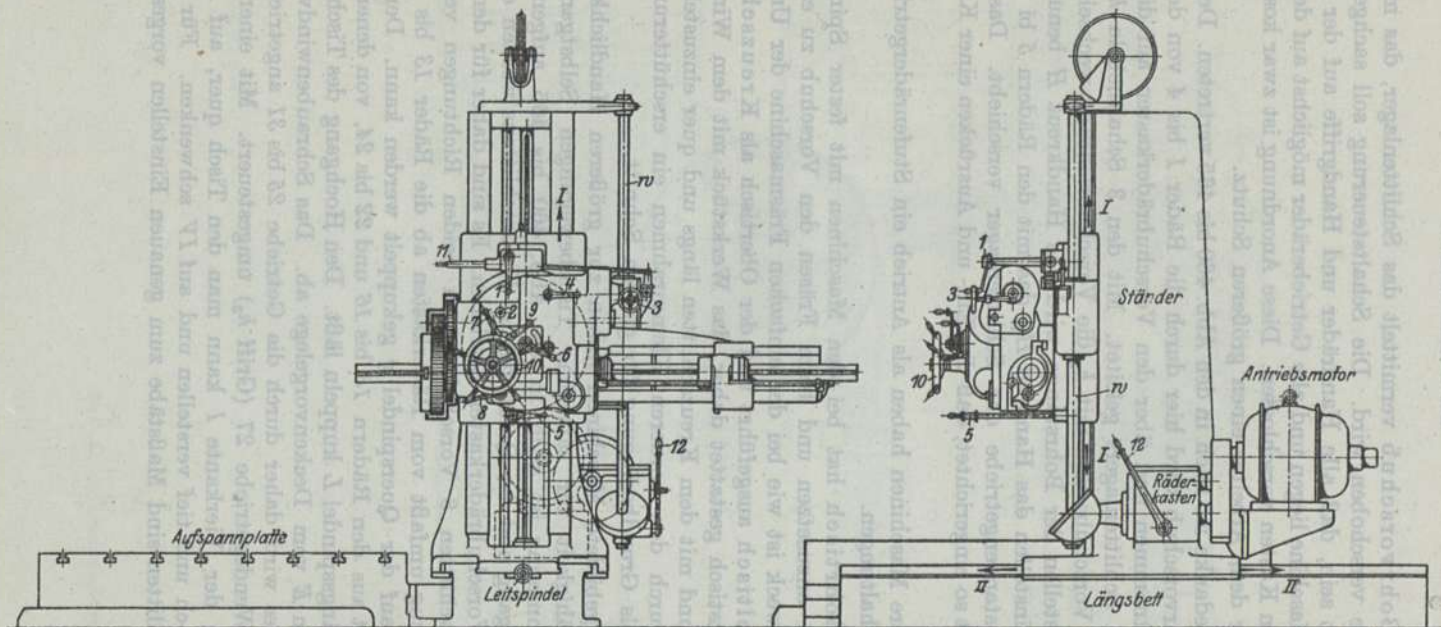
und 467. Bohr- und Fräswerk von de Fries & Co., A. G., Düsseldorf.
